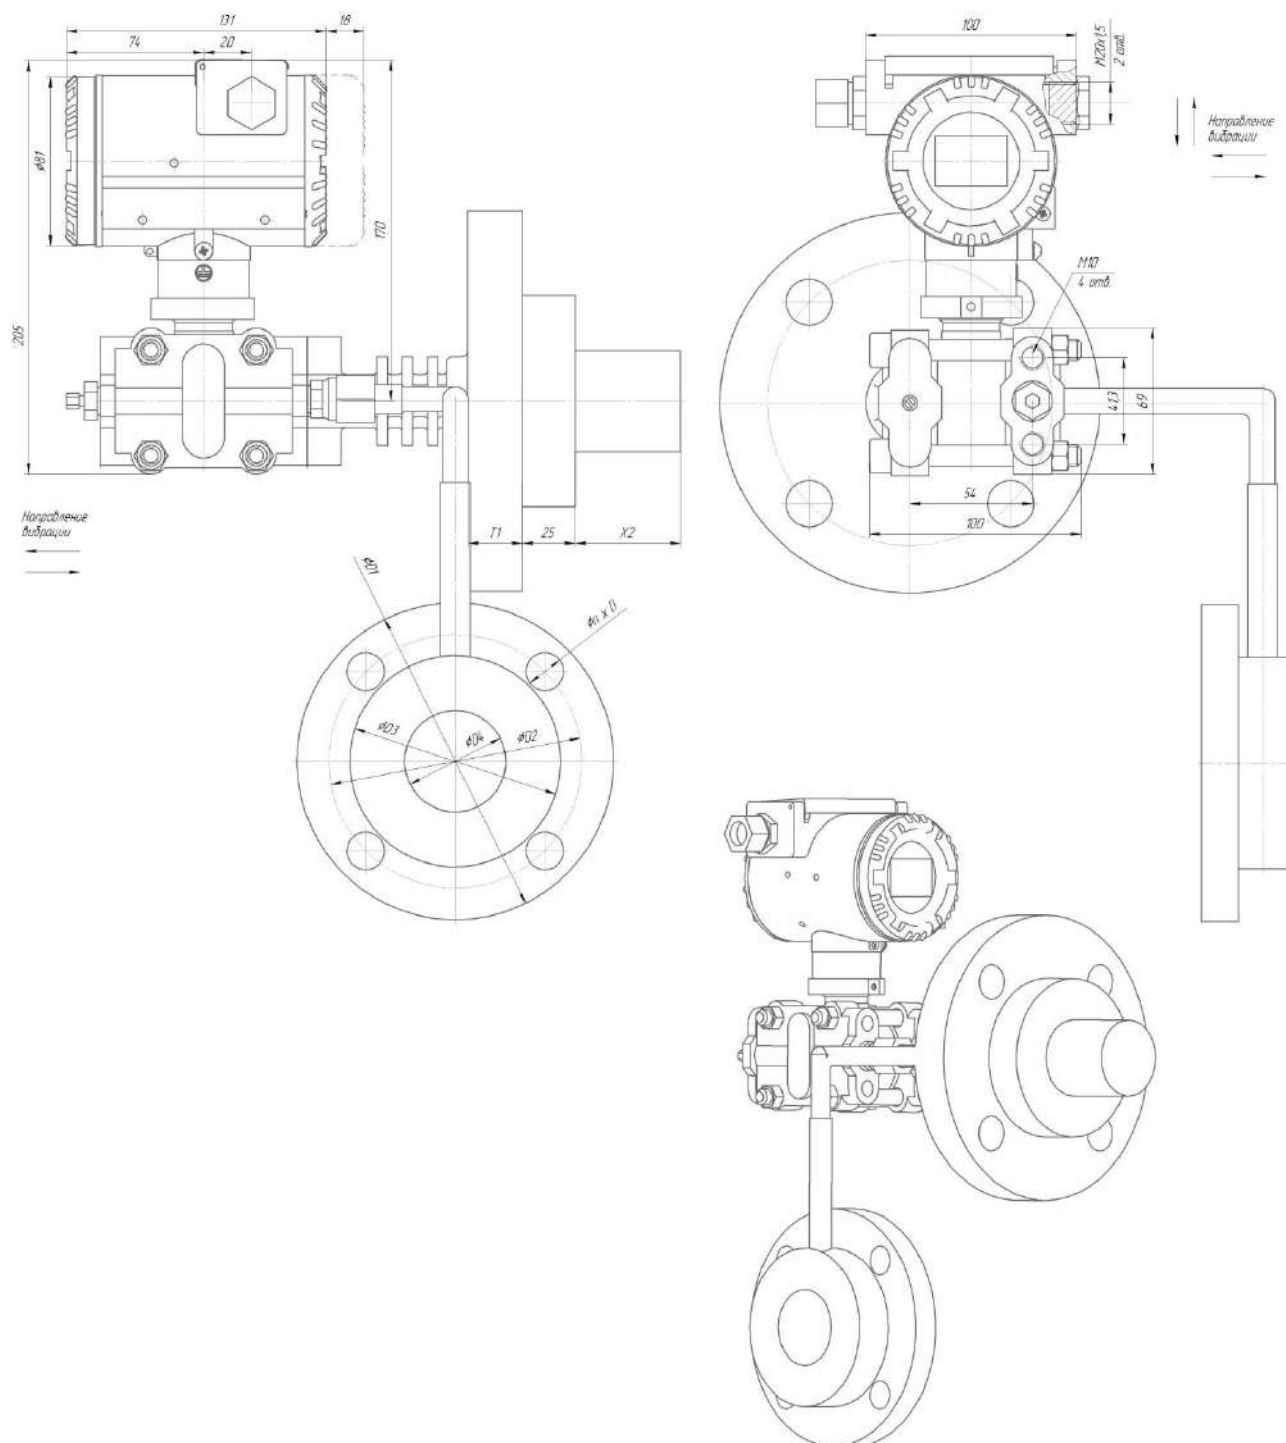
Габаритные, присоединительные размеры ЭМИС-БАР 185, 188 с нулевой длиной капилляра плюсовой камеры.
